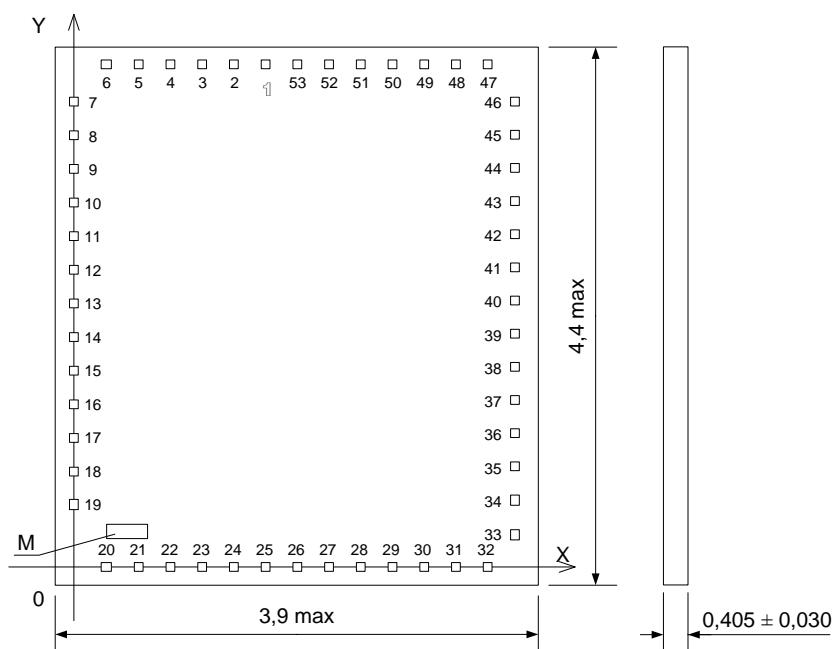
Габаритный чертеж микросхемы в корпусе H14.42-1B
